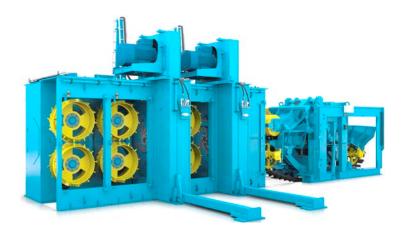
Станок VK8000-Combi-2R с двумя роторными головками
